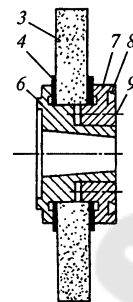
Устройства для установки и крепления шлифовальных кругов:
